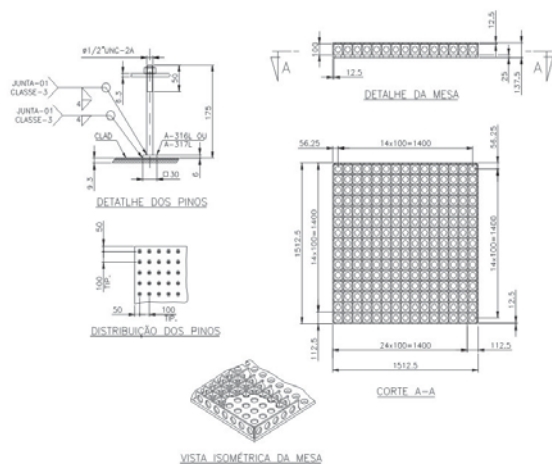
Detalhe da mesa de fixação e soldagem do revestimento
